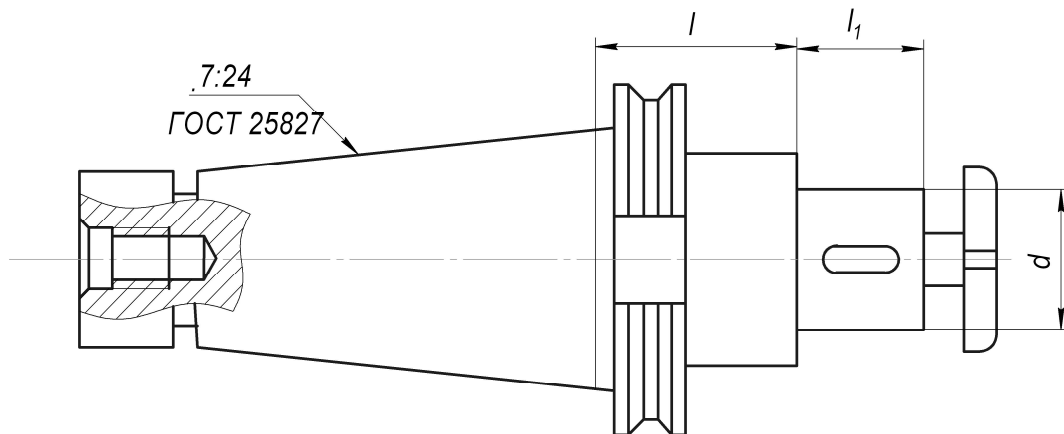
Оправка для закріплення насадних дискових і циліндричних фрез
